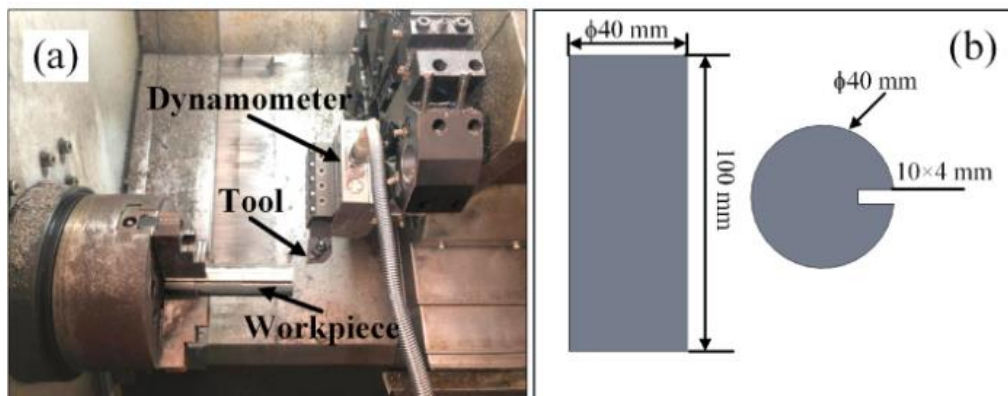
(a) Procédure de coupe (b) Dimension de la pièce à usiner.
